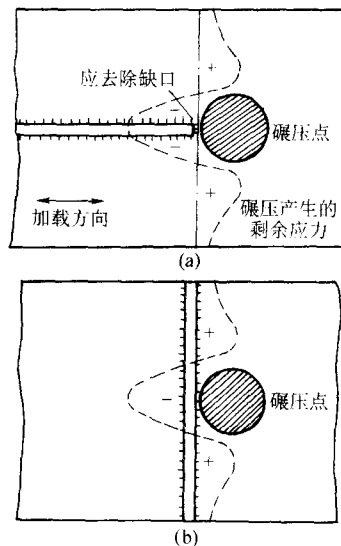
横向角焊缝的正确挤压位置
